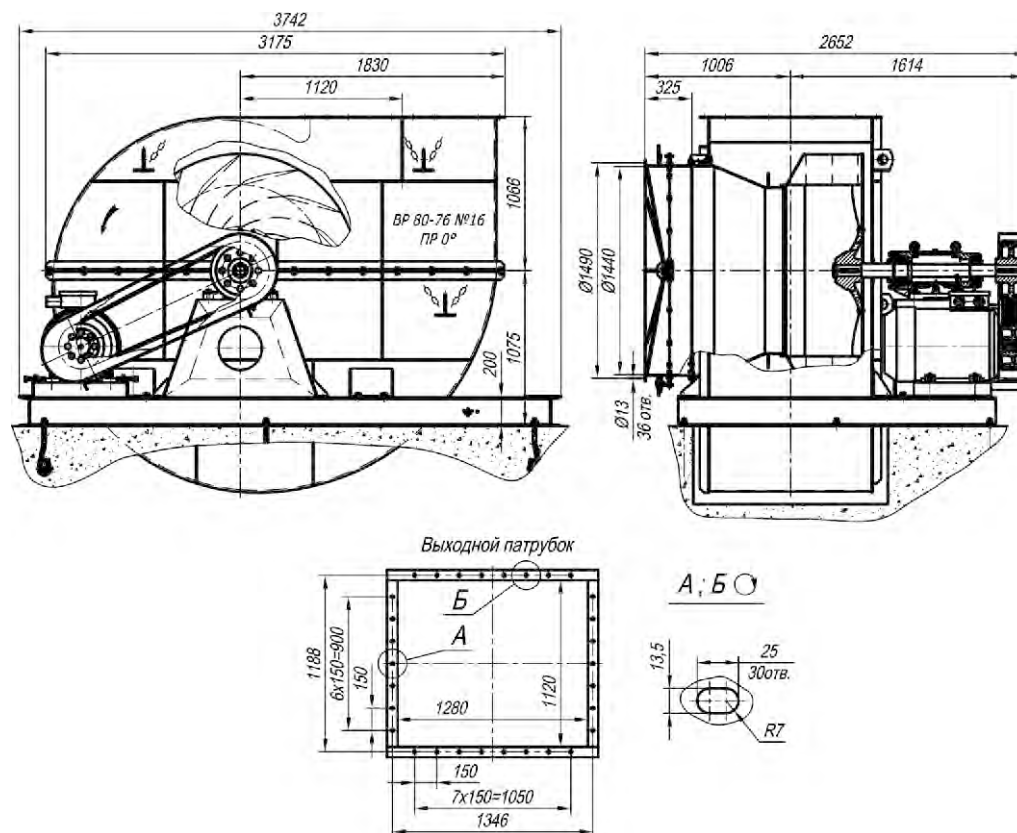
Габаритные и присоединительные размеры вентилятора ВЦ 4-76 (80-76) № 16 исп-5.
